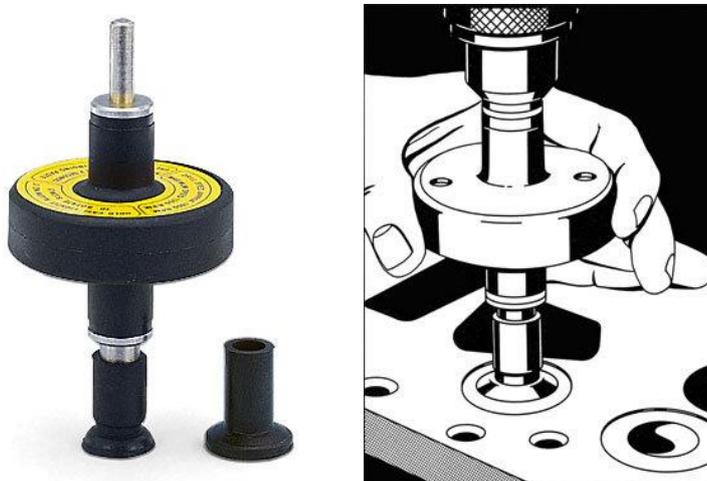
Устройство для притирки клапанов, ф. Wuerth, модели 0691.600.
